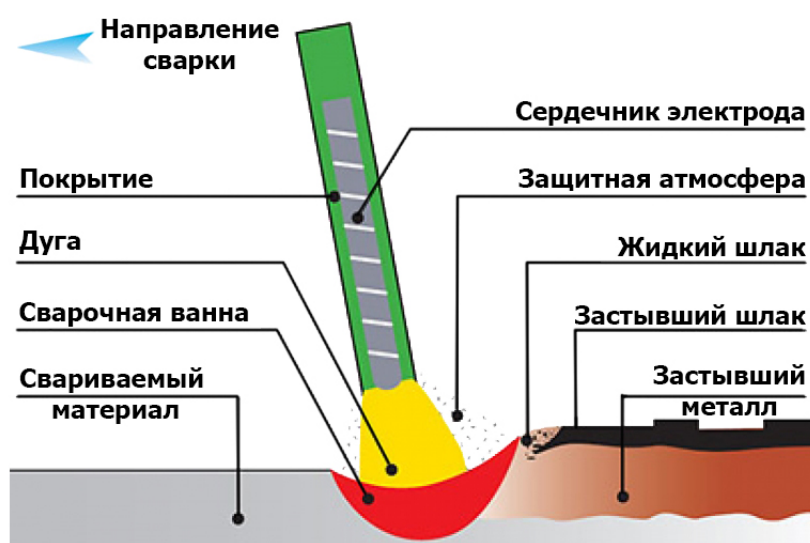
Схема процесса ручной дуговой сварки плавящимся электродом
